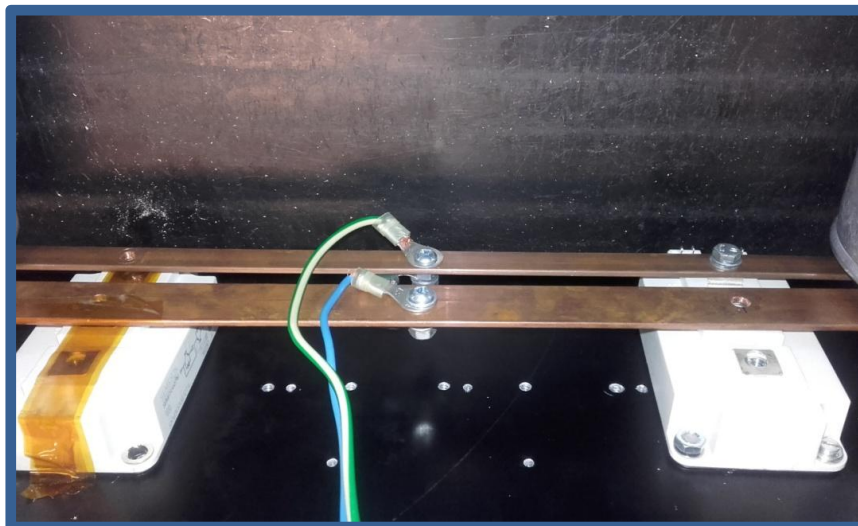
Detalle de las pletinas de conexionado durante el montaje
